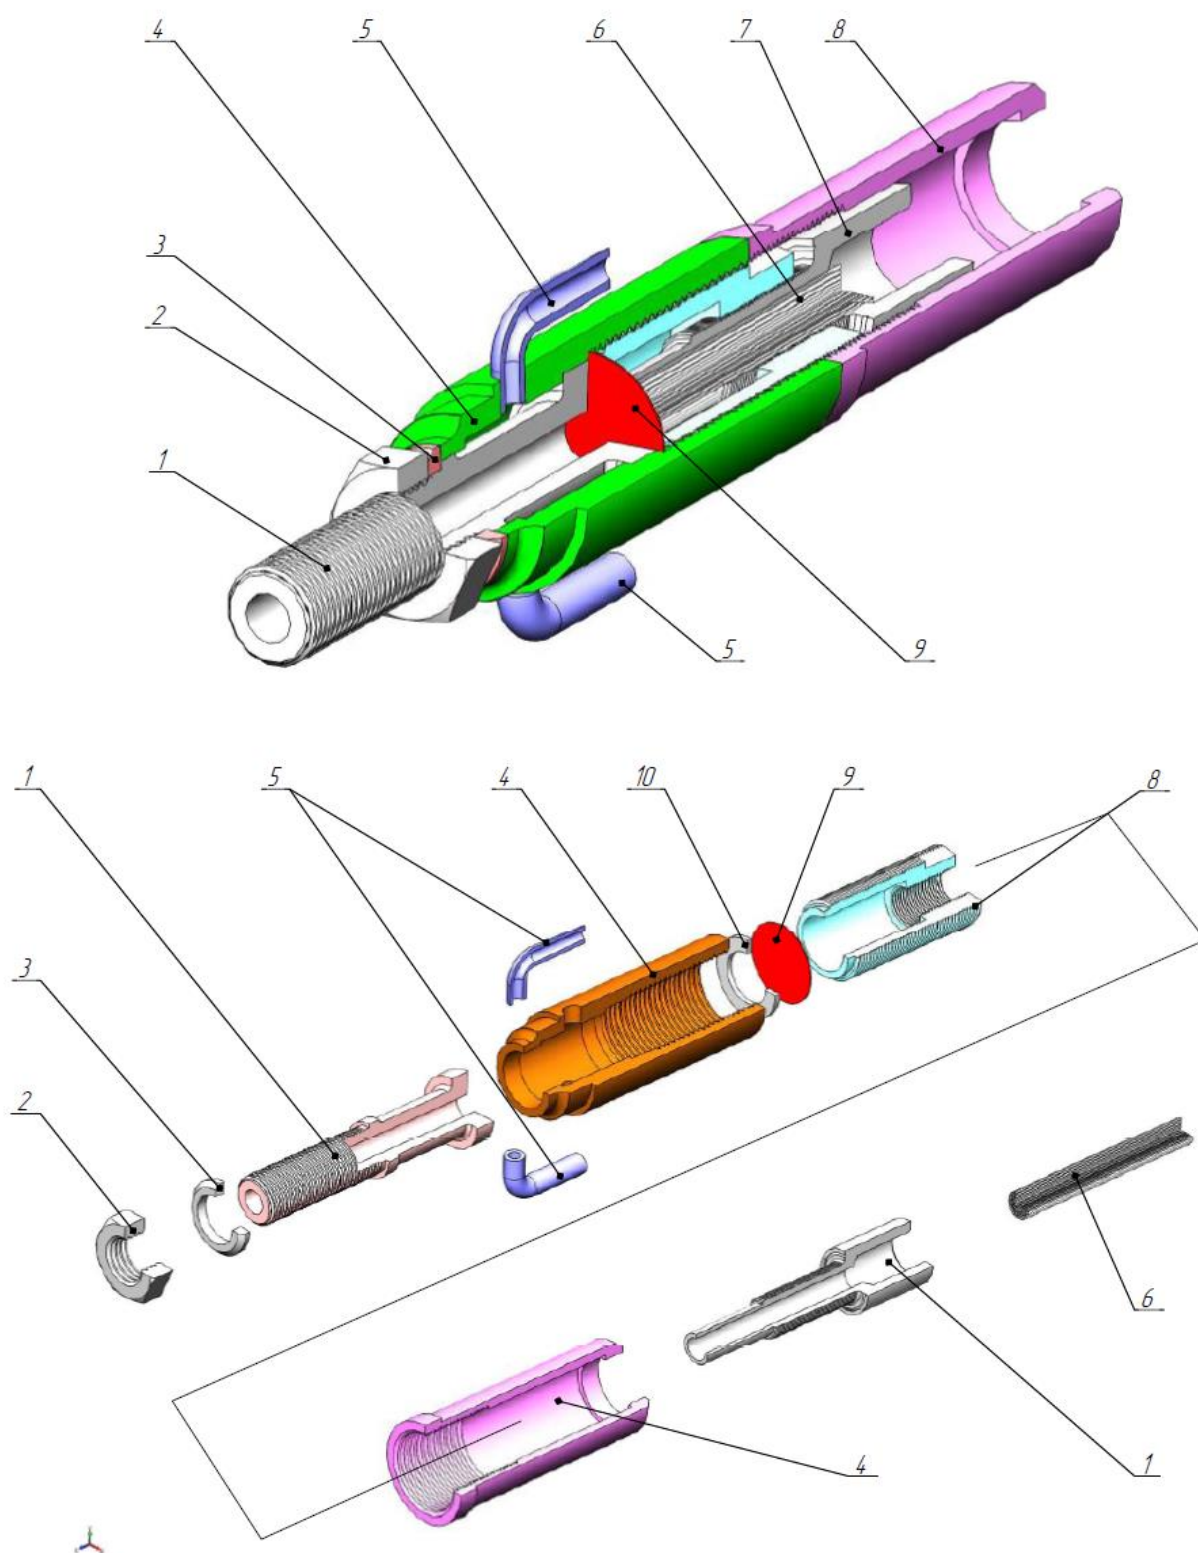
Оптиковолоконний датчик тиску: 1 – штуцер; 2 – гайка; 3, 10 – шайба; 4 – корпус; 5 – трубки; 6 – оптоволокну; 7 – обойма; 8 – кришка корпусу; 9 – діафрагма
